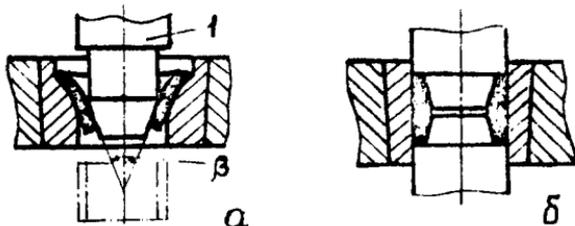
Схема технологического процесса изготовления втулок из шайбы способом вытяжки с разбортовкой: а - вытяжка с разбортовкой; б - формовка конических поверхностей.
